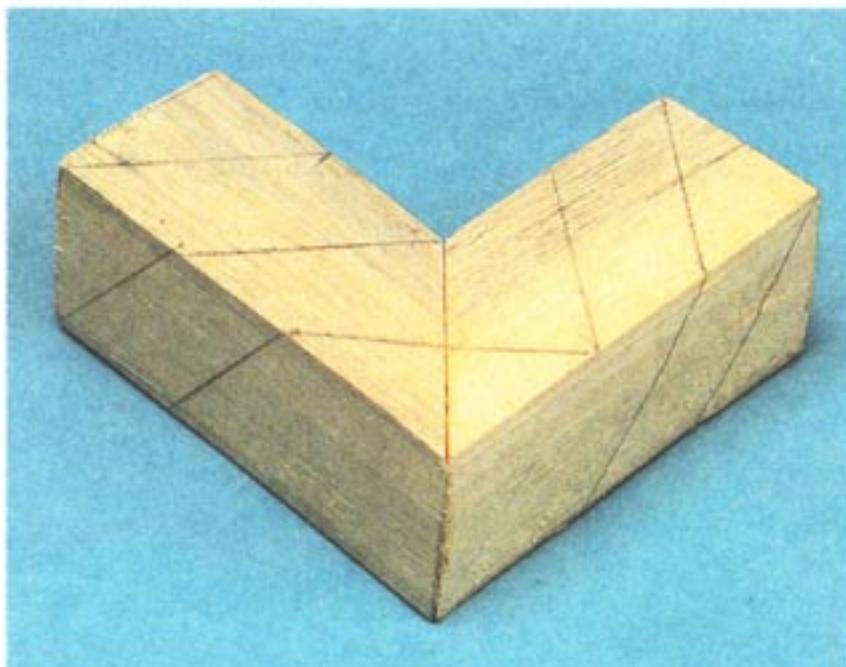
Разметка заготовки из двух деталей (вид сзади)
